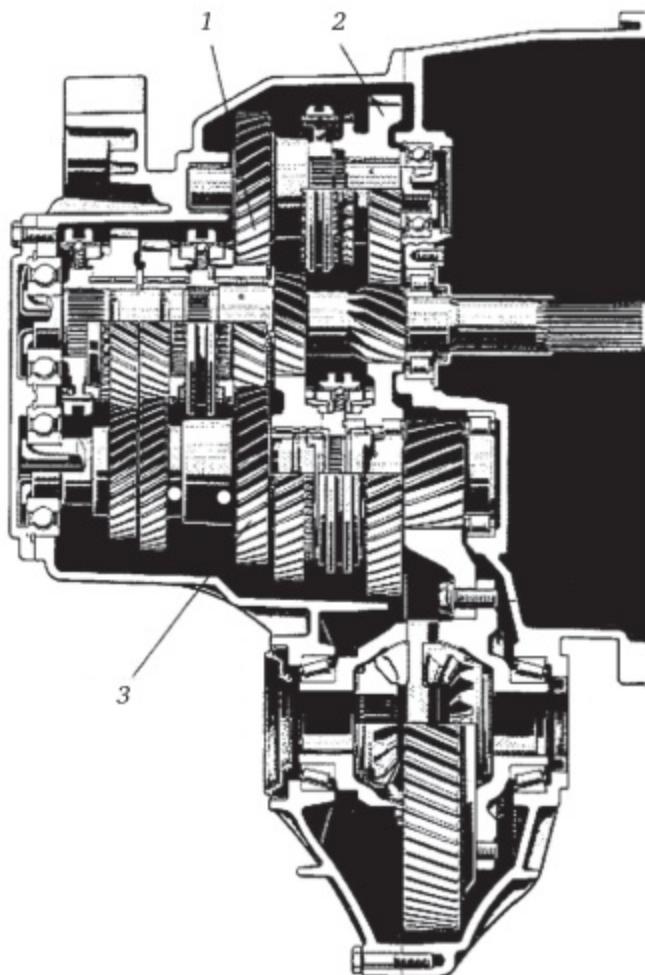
2-вальная коробка передач с уменьшенными осевыми габаритами
